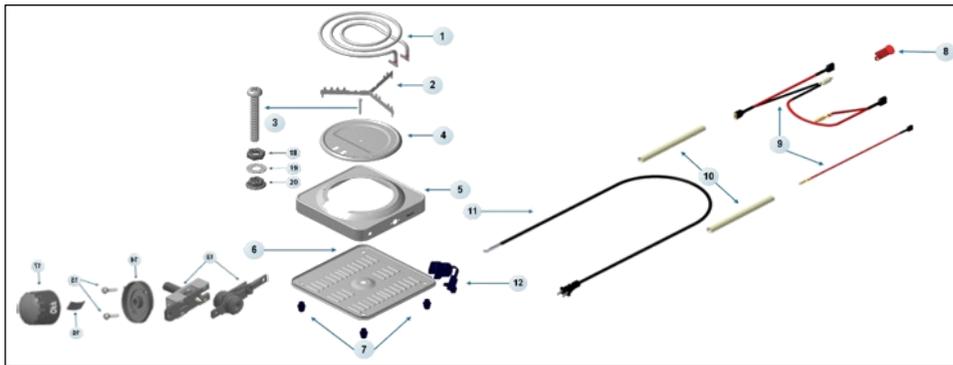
Diseño explosionado de la parrilla eléctrica marca “Taurus” diseñado en MasterCAM.
